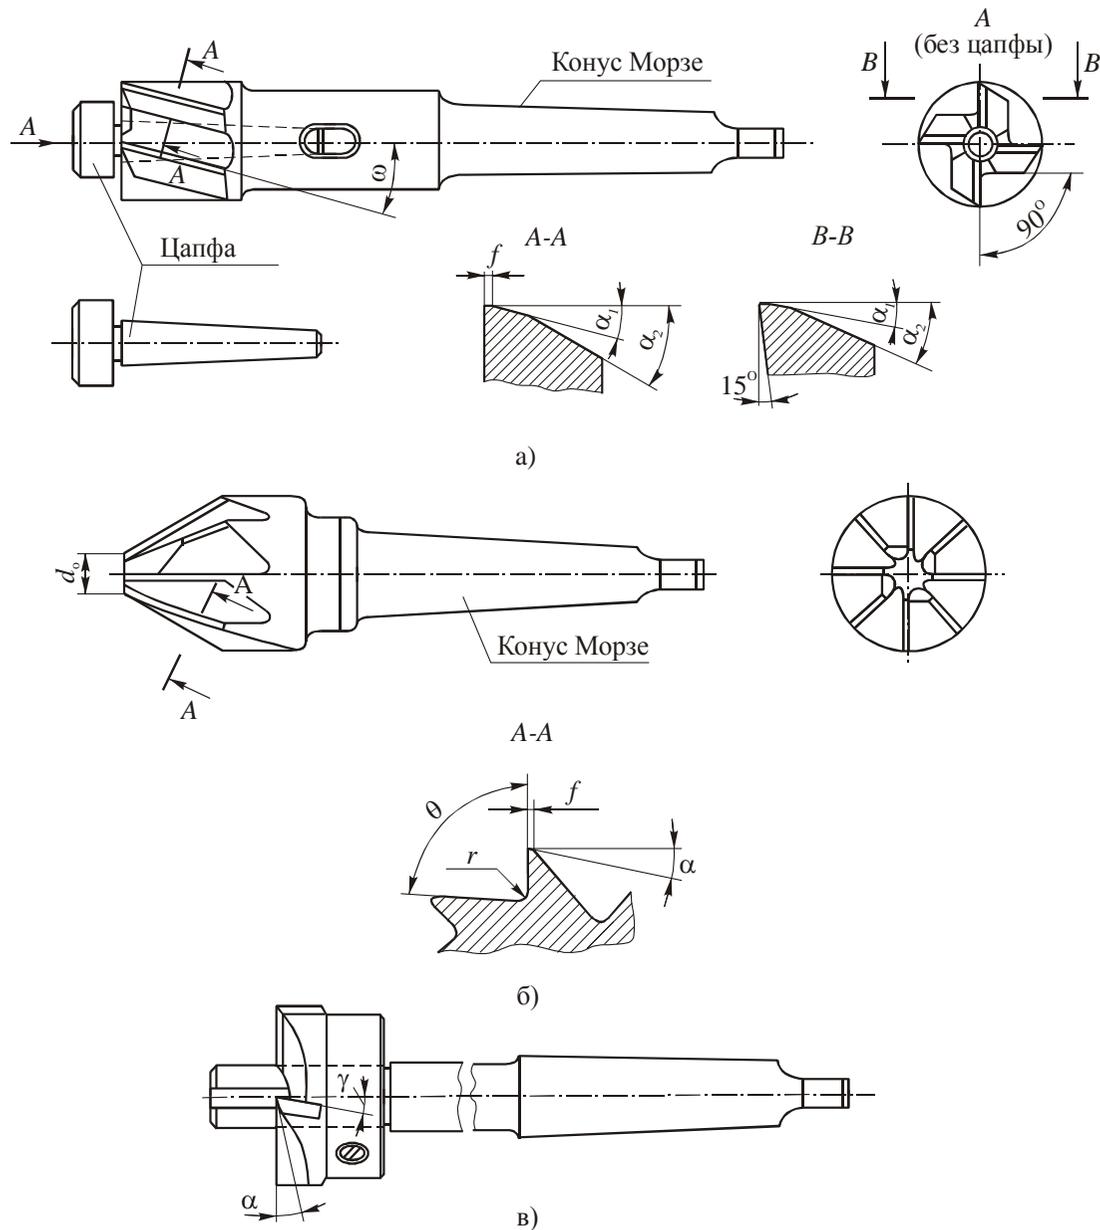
Зенковки: *а* – для цилиндрических углублений; *б* – для конических углублений; *в* – для подрезки торцов
